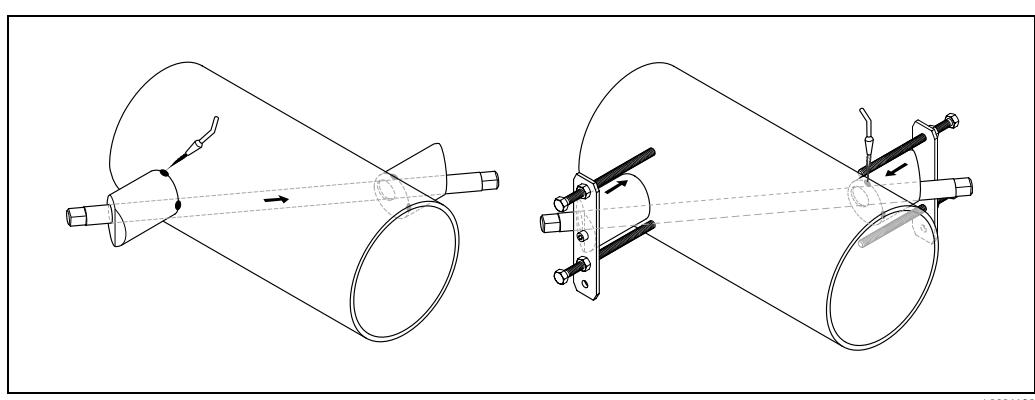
Instalarea senzorilor de masurare, pasul 9
